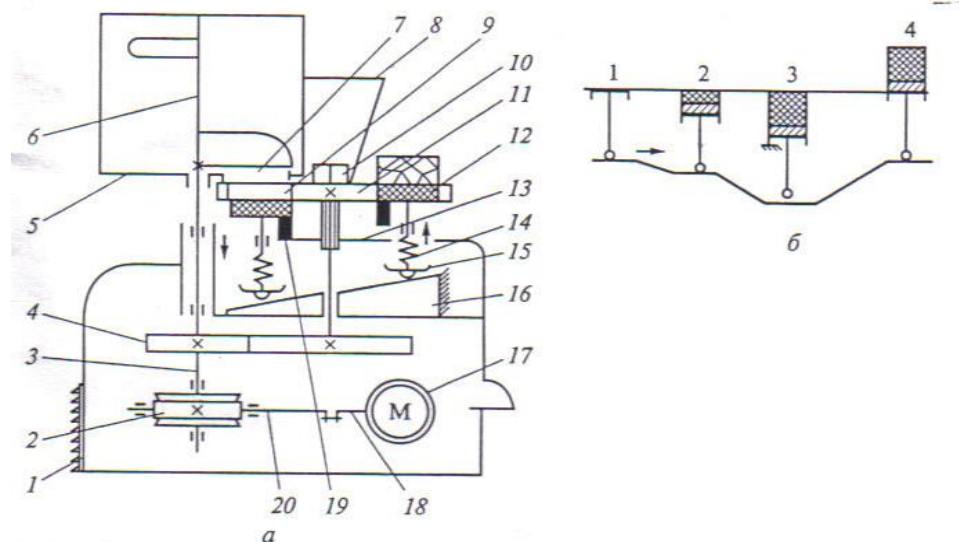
Котлетоформовочная машина МФК-2240: а – кинематическая схема; б – циклограмма движения поршня формующего стола; 1 – корпус; 2 – червячный редуктор; 3 – вал шнека-питателя; 4 – зубчатая цилиндрическая передача; 5 – бункер для фарша; 6 – шнек-питатель; 7 – окно бункера; 8 – бункер для панировочный сухарей; 9 – отверстие-ячейка; 10 – регулировочный винт; 11 – формующий стол; 12 – поршень; 13 – планка; 14 – пружины; 15 – толкатель; 16 – торцевой диск-копир; 17 – электродвигатель; 18 – вал электродвигателя; 19 – упор; 20 – вал червячного редуктора
